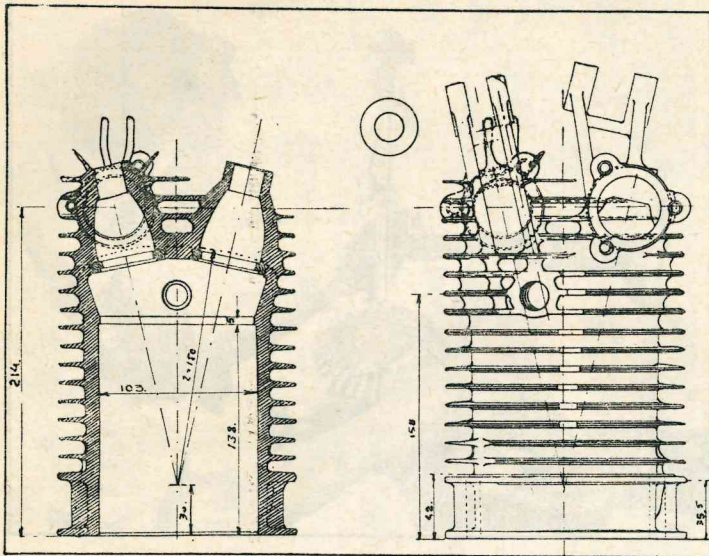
Цилиндр малого авиа-мотора для авиетты, отлитый под давлением (алюминиевый сплав).
